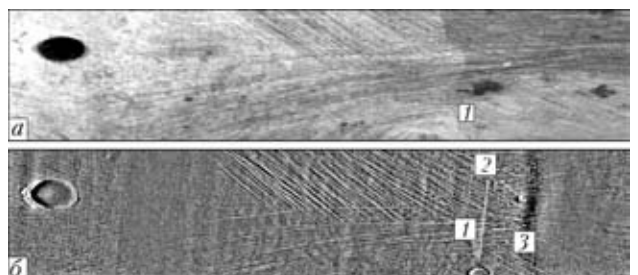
Сварной шов без поверхностных дефектов (зачистка с лицевой стороны): *a* — фотография поверхности тест-образца; *б* — МОВ МГ тест-образца (1 — кромка сварного шва; 2 — подповерхностные пузырьки воздуха; 3 — область корня шва)
